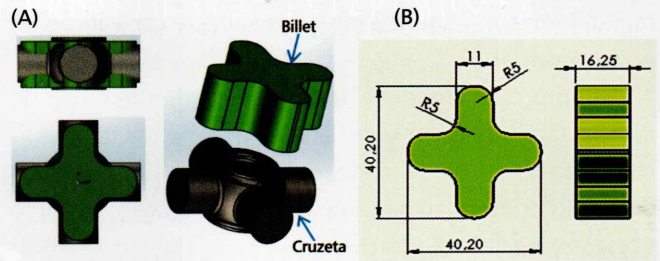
Desenho de construção do billet (A) e suas dimensões (B).
